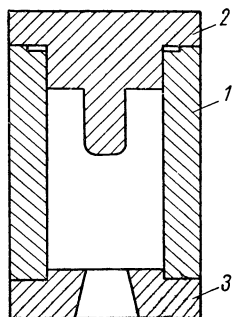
Форма для литья под давлением с неразъемным корпусом.
